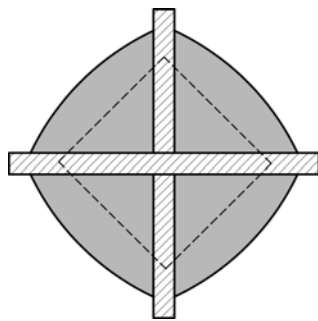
Поперечний переріз деталі для виготовлення зразка зварного шва
